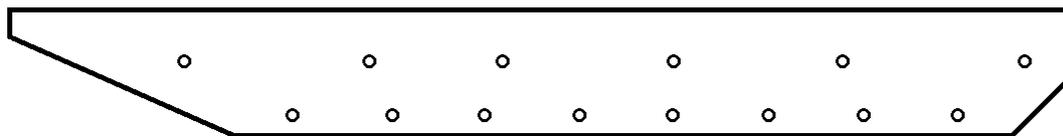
Герметичный полый корпус тягача (вид сбоку)
